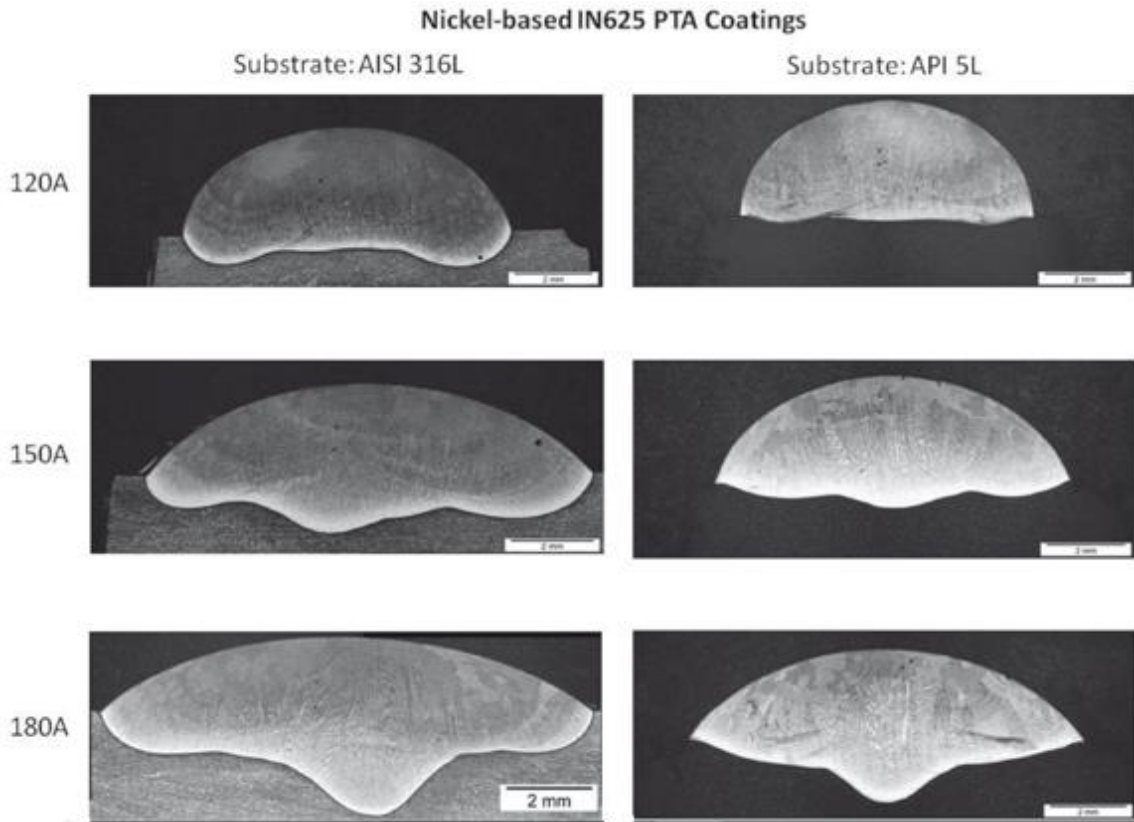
Geometría del cordón de soldadura para diferente metal base y amperaje [34]
